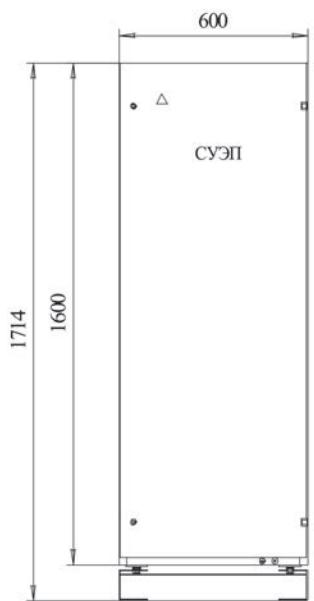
Габаритный чертеж СУЭП-3-В (глубина стойки 600мм)
